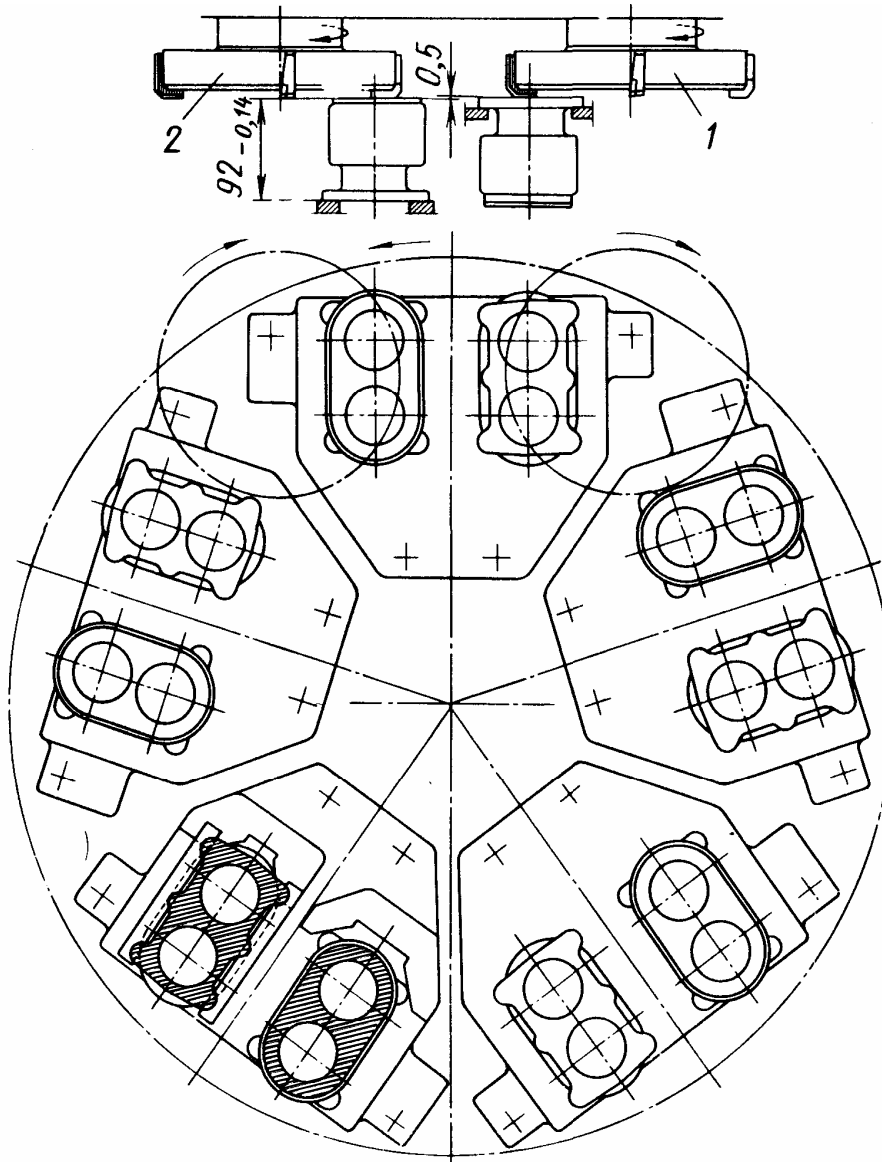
Схема фрезерування торців заготовок на двошпindelному фрезерному верстаті з обертвовим столом: 1 – чорнова фреза; 2 – чистова фреза
